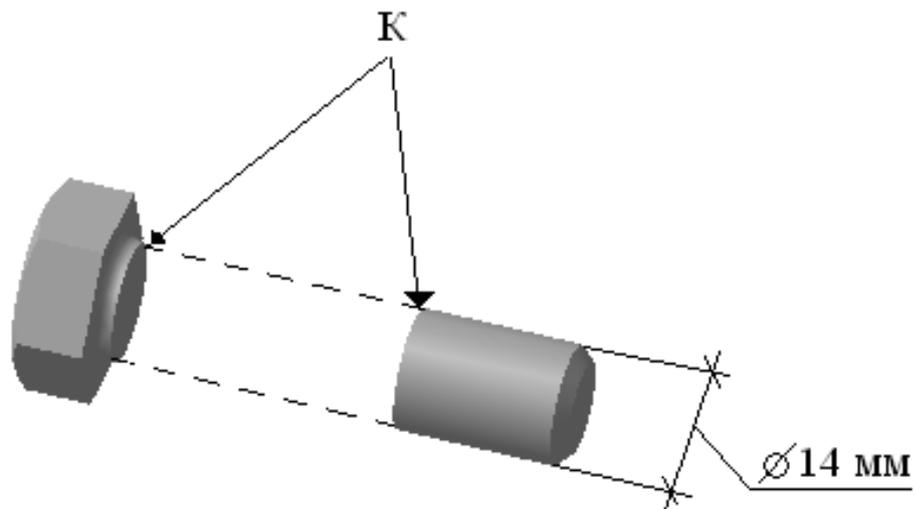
Схема для расчета болта (М14×1,5) на срез
